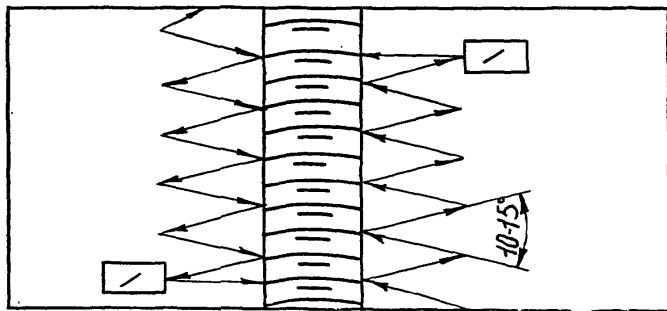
Схема перемещения искателя по поверхности при контроле сварного шва
